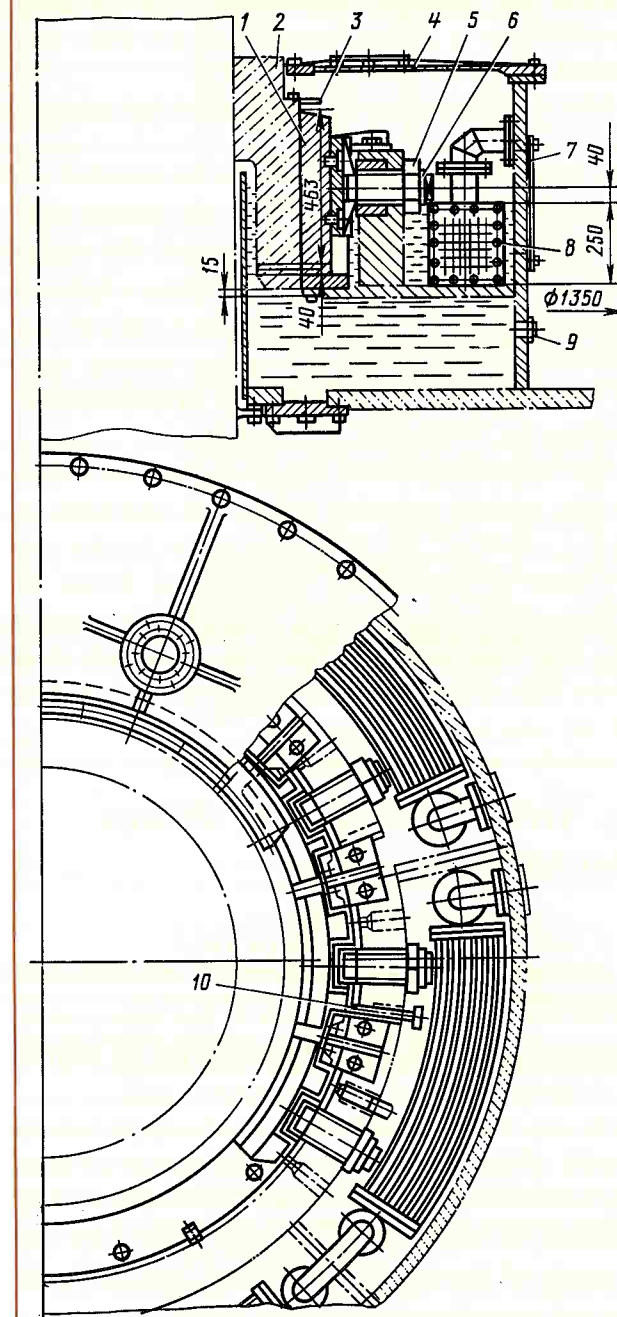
Разрез по узлу подшипника с самоустанавливающимися сегментами с винтовой опорой:
